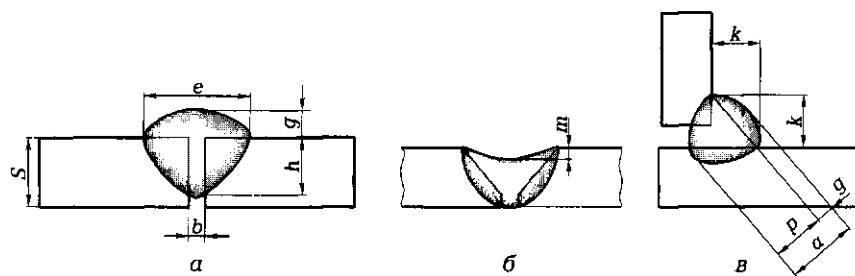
Основные геометрические параметрыстыковых (а, б) и углового (в) сварных швов:
